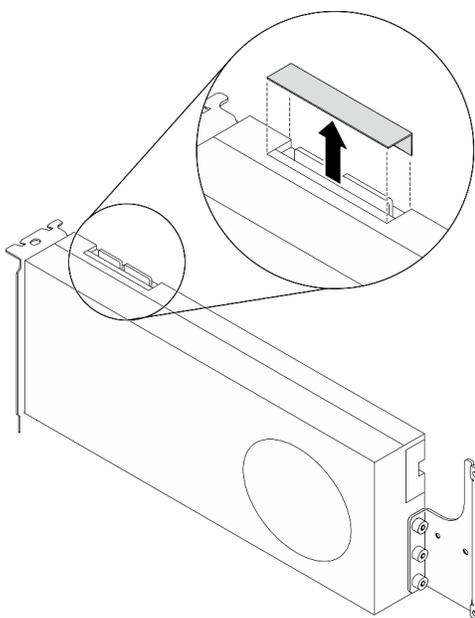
Rimozione del coperchio del coperchio del connettore di collegamento dalla GPU
